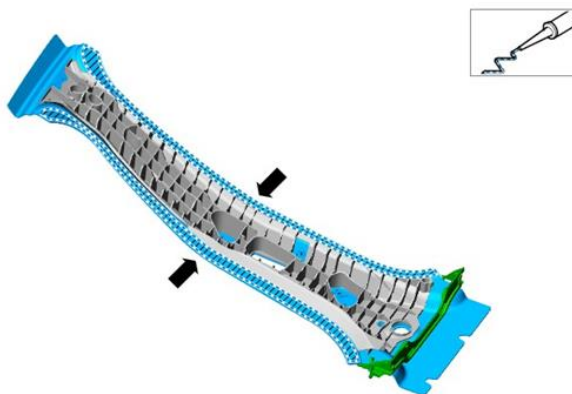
Zonas de aplicación de adhesivo en la unión. Fuente: CESVIMAP
